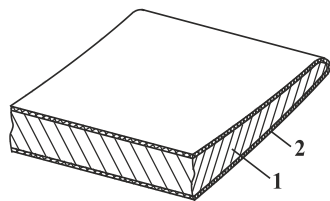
Элемент лопатки компрессора с ионно-плазменным покрытием
